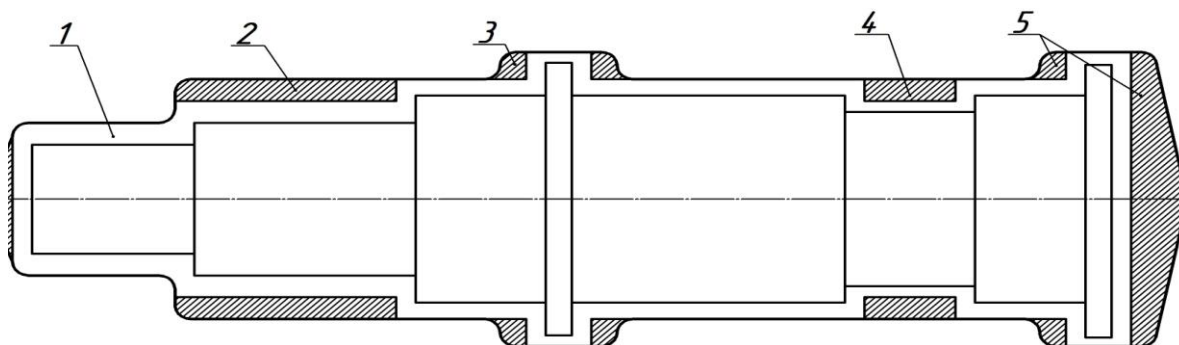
Схема розташування напусків на поковці типу вала:
